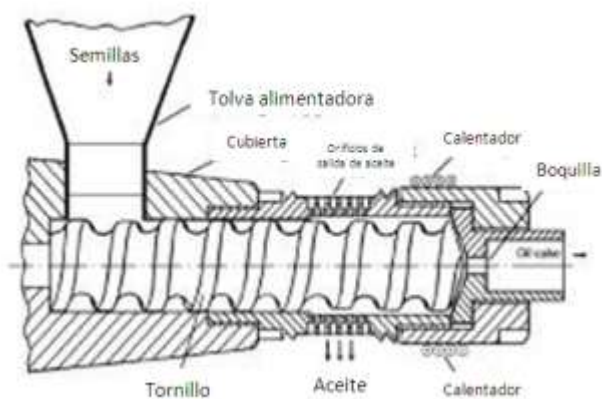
Dibujo esquemático de una prensa de cilindro agujereado. Nótese que la boquilla puede ser cambiada [4].
